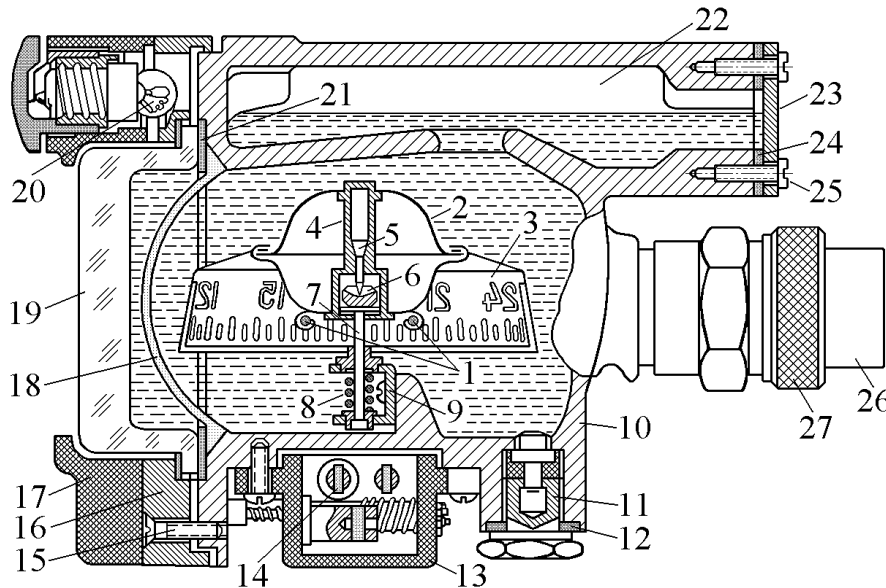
Компас КИ-11: 1 – подвижные магниты; 2 – поплавок; 3 – шкала; 4 – втулка; 5 – шпилька; 6 – топка; 7 – колонка; 8 – амортизационная пружина; 9 – скоба; 10 – котелок; 11 – пробка наливного отверстия; 12 – свинцовая прокладка; 13 – корпус девиационного прибора; 14 – девиационный магнит; 15 – винт крепления стекла; 16 – кольцо крепления стекла; 17 – декоративное кольцо; 18 – курсовая черта; 19 – стекло; 20 – лампочка; 21 – прокладка; 22 – компенсационная камера; 23 – крышка; 24 – прокладка; 25 – винт крепления крышки; 26 – штепсель; 27 – накидная гайка
